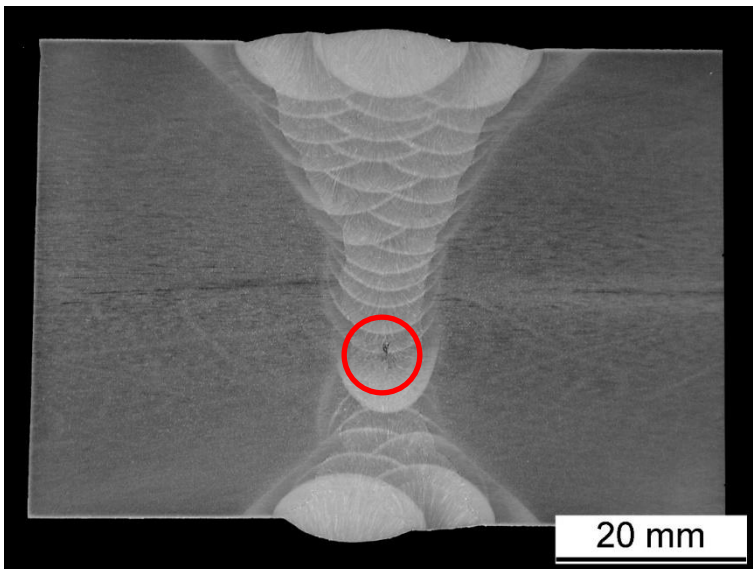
Makroschliff des ersten Schweißversuches (Markierung: Unregelmäßigkeit gemäß DIN EN ISO 5817: ungenügende Durchschweißung)
